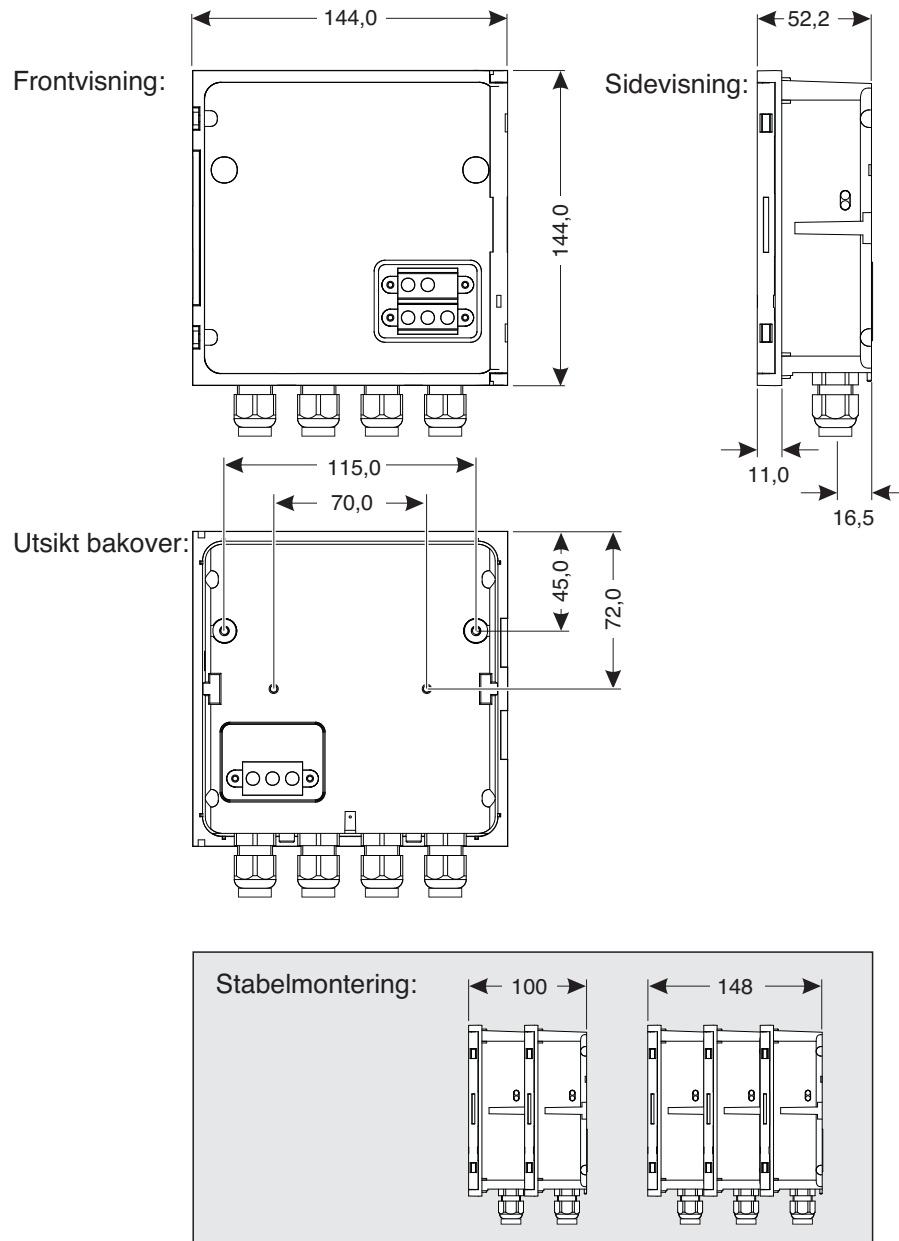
Dimensjonstegning av MIQ-modul (dimensjoner i mm)
